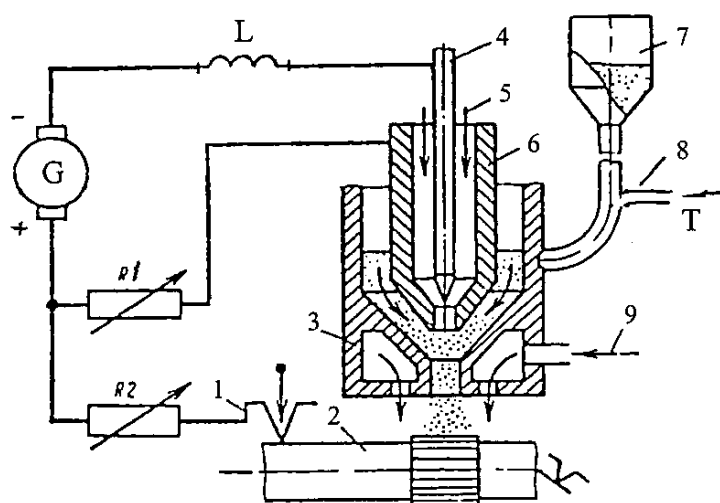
Схема наплавки с вдуванием порошка в плазменную струю: 1 – провод; 2 – деталь; 3 – наружное сопло; 4 – вольфрамовый катод; 5 – плазмообразующий газ; 6 – внутренне сопло; 7 – питатель; 8 – транспортирующий газ; 9 – защитный газ; G – источники питания током; R1 и R2 – реостаты; L – дроссель
